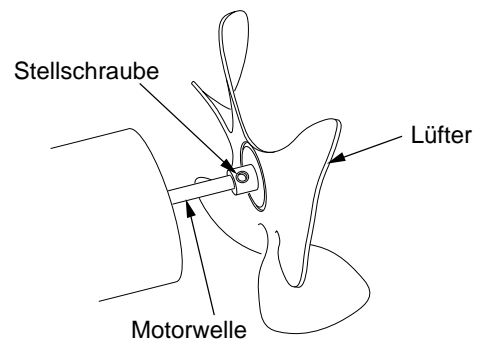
Lage von Lüfter, Motorwelle und Stellschraube
